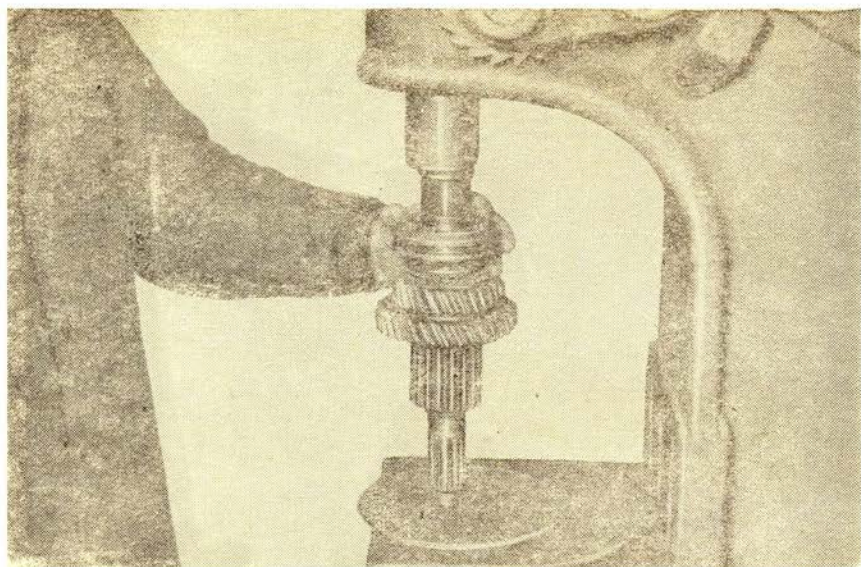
Напрессовка скользящей муфты со ступицей на ведомый вал
